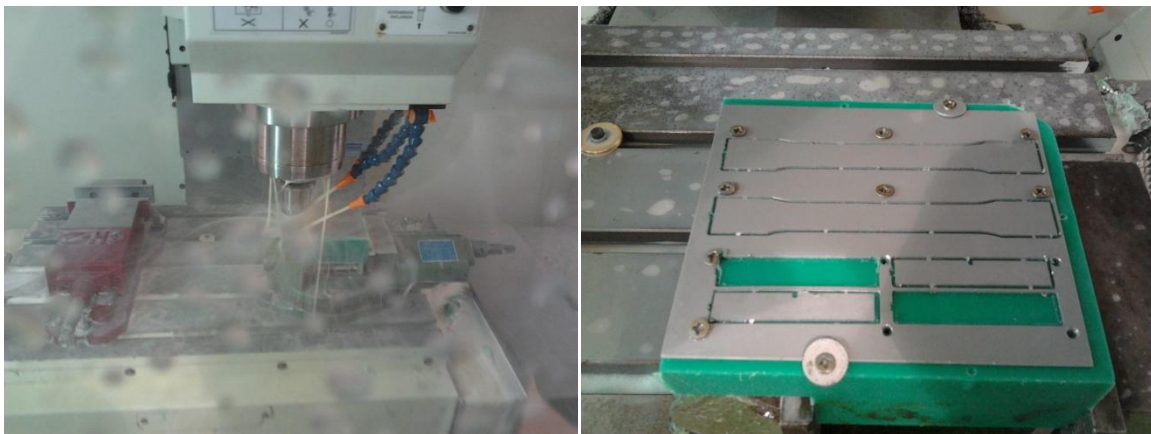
Mecanizado de las probetas (izquierda) y resultado final (derecha)
